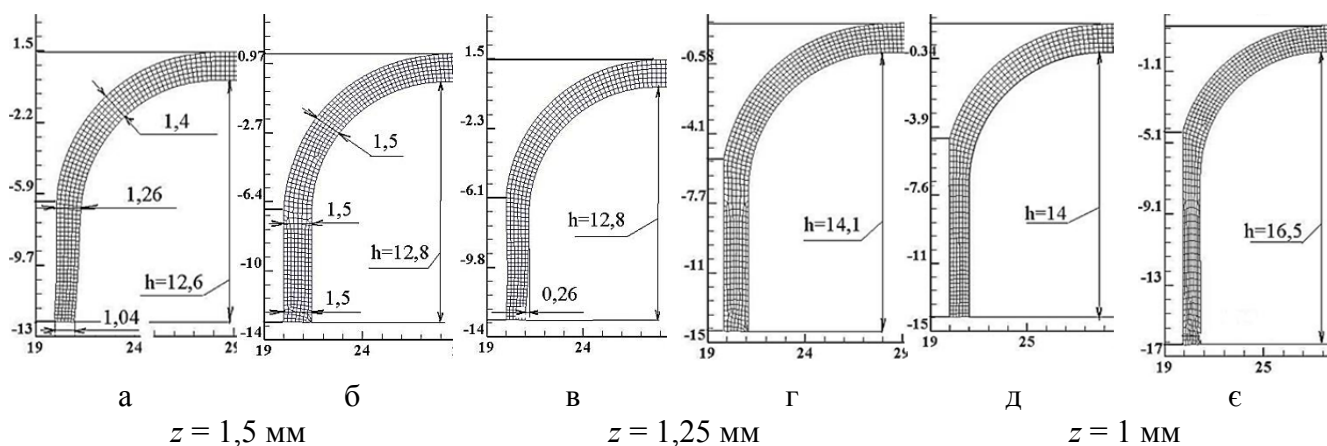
Форма і розміри zdeформованих частин заготовок (розміри в міліметрах):
